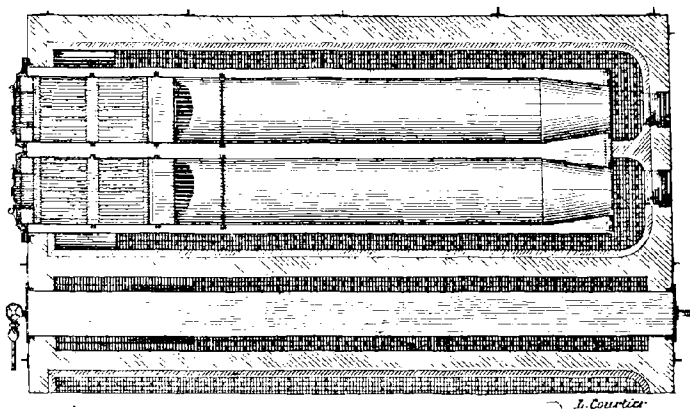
Chaudière de Lancastre (coupe horizontale).
